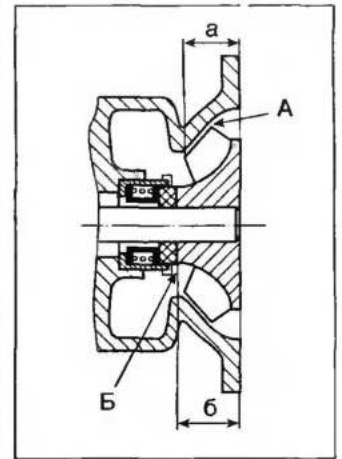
Размерная цепь при установке крыльчатки - размеры а и б от фланца должны быть такими, чтобы обеспечить зазор между колесом и корпусом (А) и поджатие графитового кольца к торцу крыльчатки (Б)
